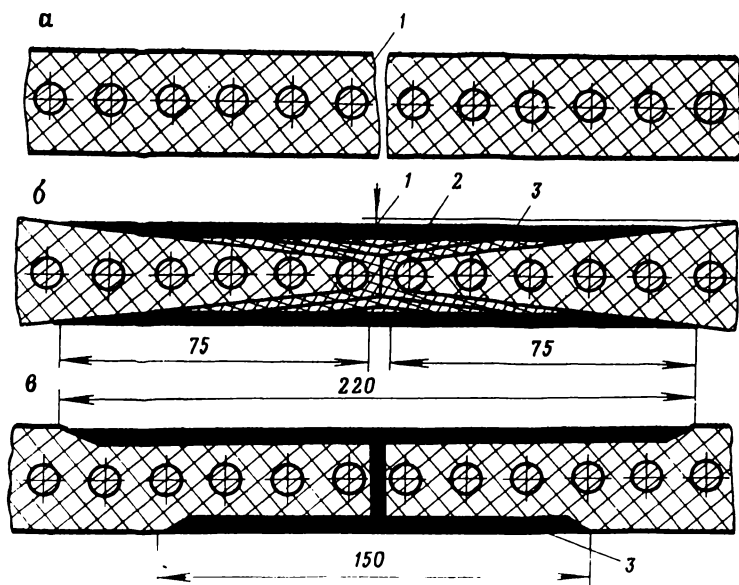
Схема ремонта продольного порыва резинокросовой ленты:
